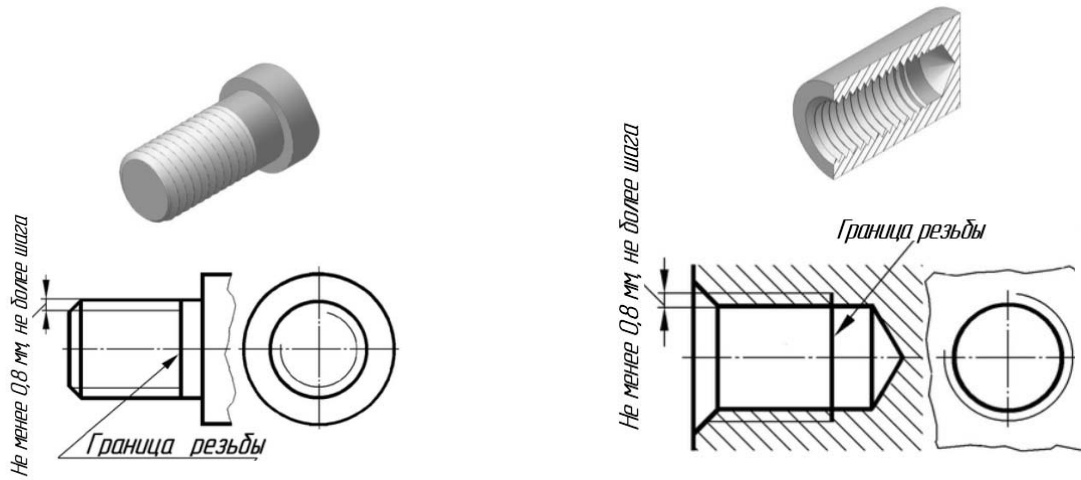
Изображение резьбы на цилиндрических поверхностях
